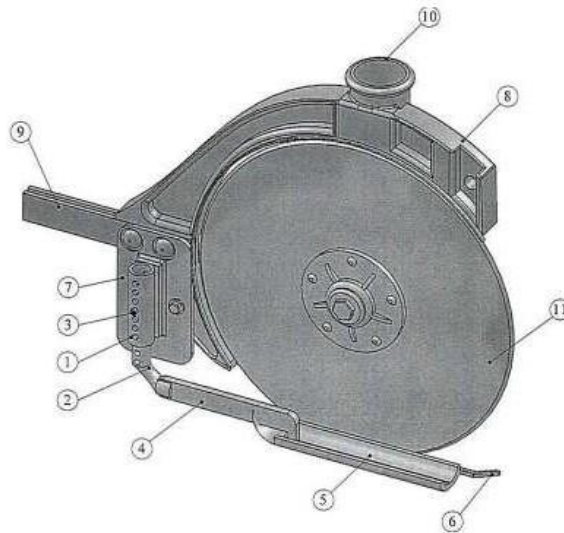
Дводисковий сошник: 1 - втулка; 2 - регулювальний палець; 3 - обмежувальний болт; 4 - брус; 5 - опорна лижа; 6 - загортач; 7 - пластина; 8 - корпус, 9 - повідок, 10 - прийомна воронка; 11 - диски
